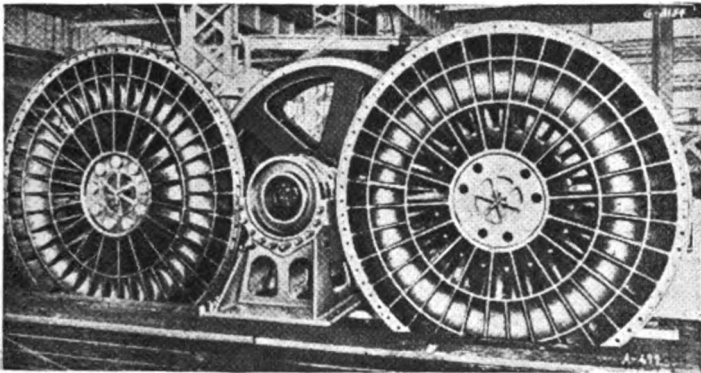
Acoplamiento hidráulico y reductor a engranajes para un buque motor de 6000 HP.
